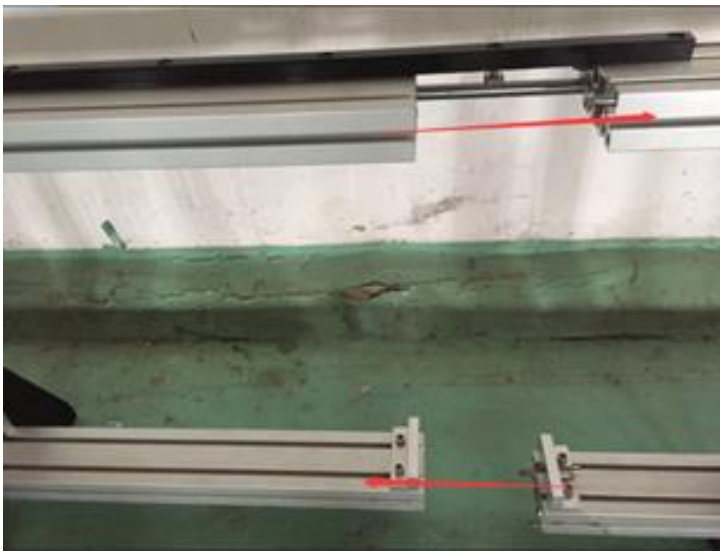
Стыковка секций бокового рельса 6-ти метрового станка (2500x6000)
